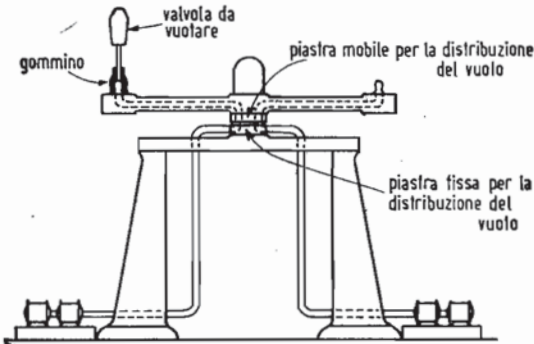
Disegno di principio della macchina per la vuotatura dei tubi.
